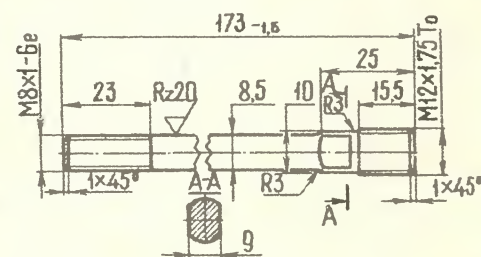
Ремонтная шпилька для крепления цилиндра и головки.
